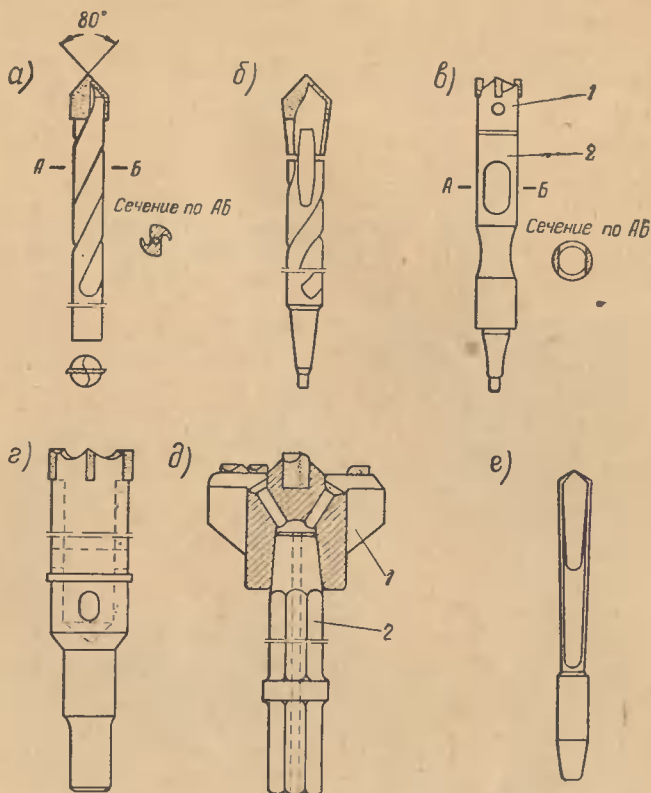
Рабочие инструменты для выполнения отверстий в неметаллических материалах; а — сверло спиральное конструкции «Укртвердосплав»; б — сверло спиральное со сменной головкой; в — бур сверлильный пустотельный; г — шлямбур конструкции «Укртвердосплав»; д — коронка съемная со штангой; е — пробойник ручной.
